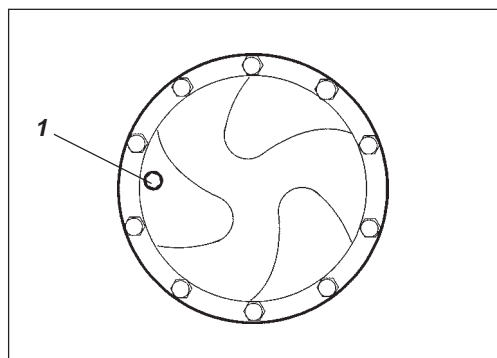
Contrôle de niveau – réducteur planétaire (CA 262-362 Std.)
